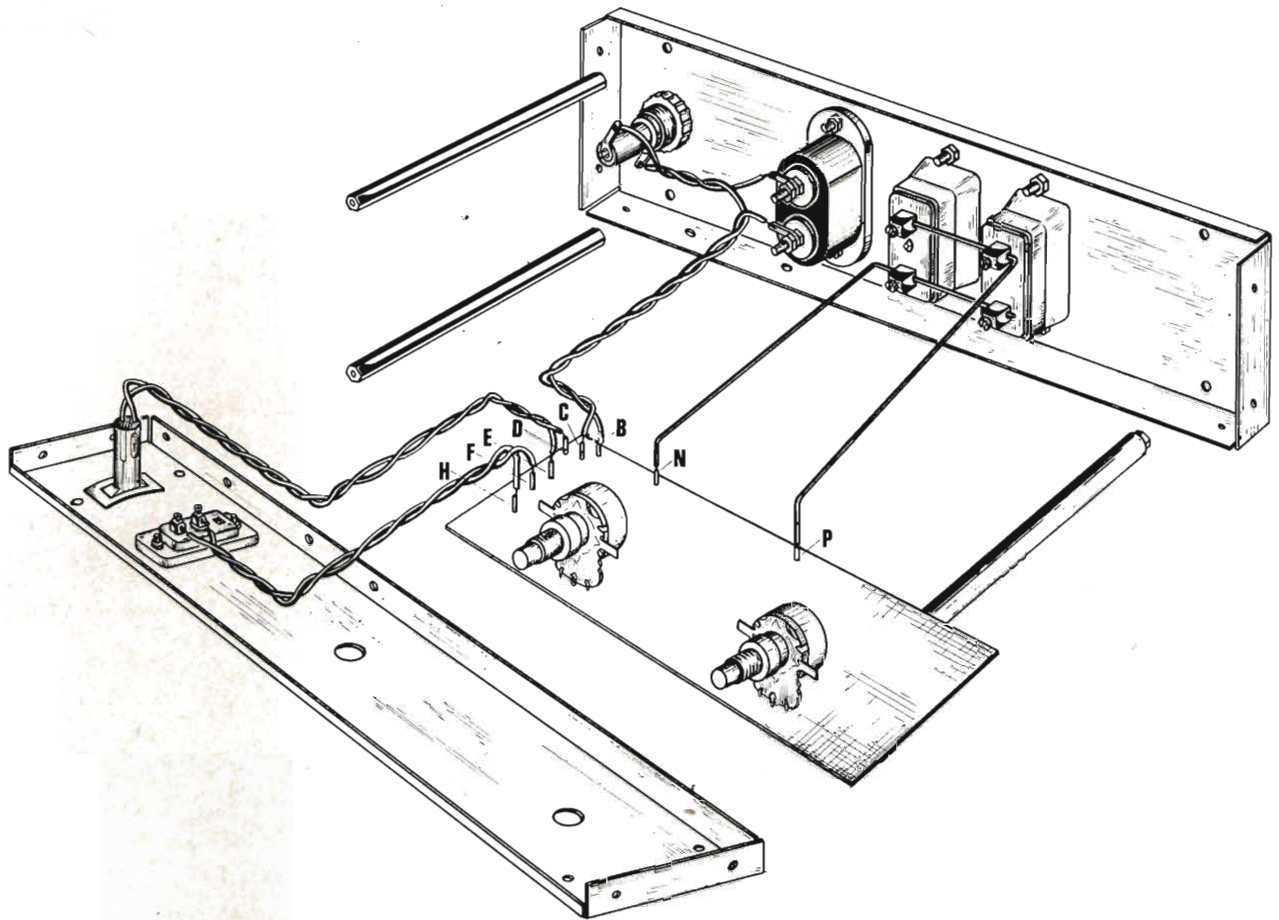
Cablaggio fra circuito stampato e pannelli.
